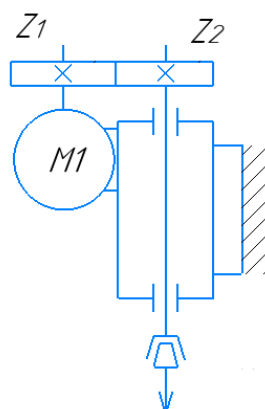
Кінематична схема силовій головки для фрезерування фаски
